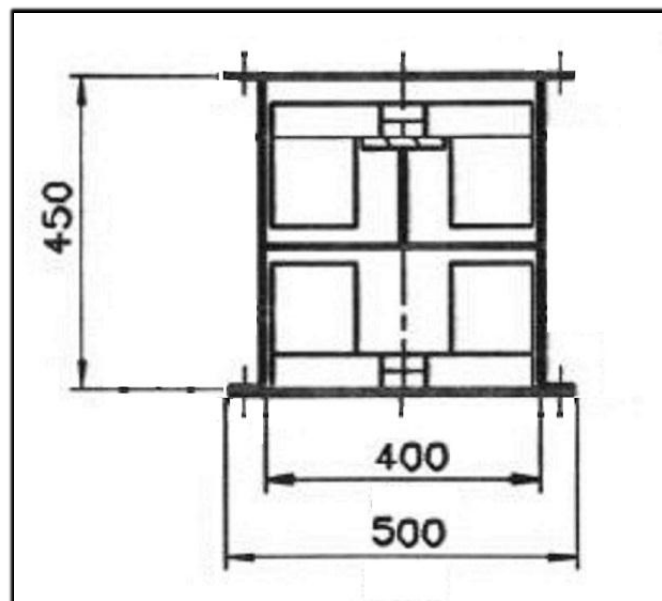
Vista sección transversal de carcaza de la transportadora.
